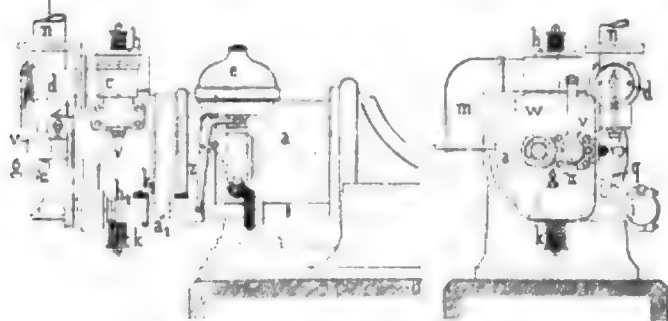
Gasmotor der Gasmotoren-Fabrik Deutz.
